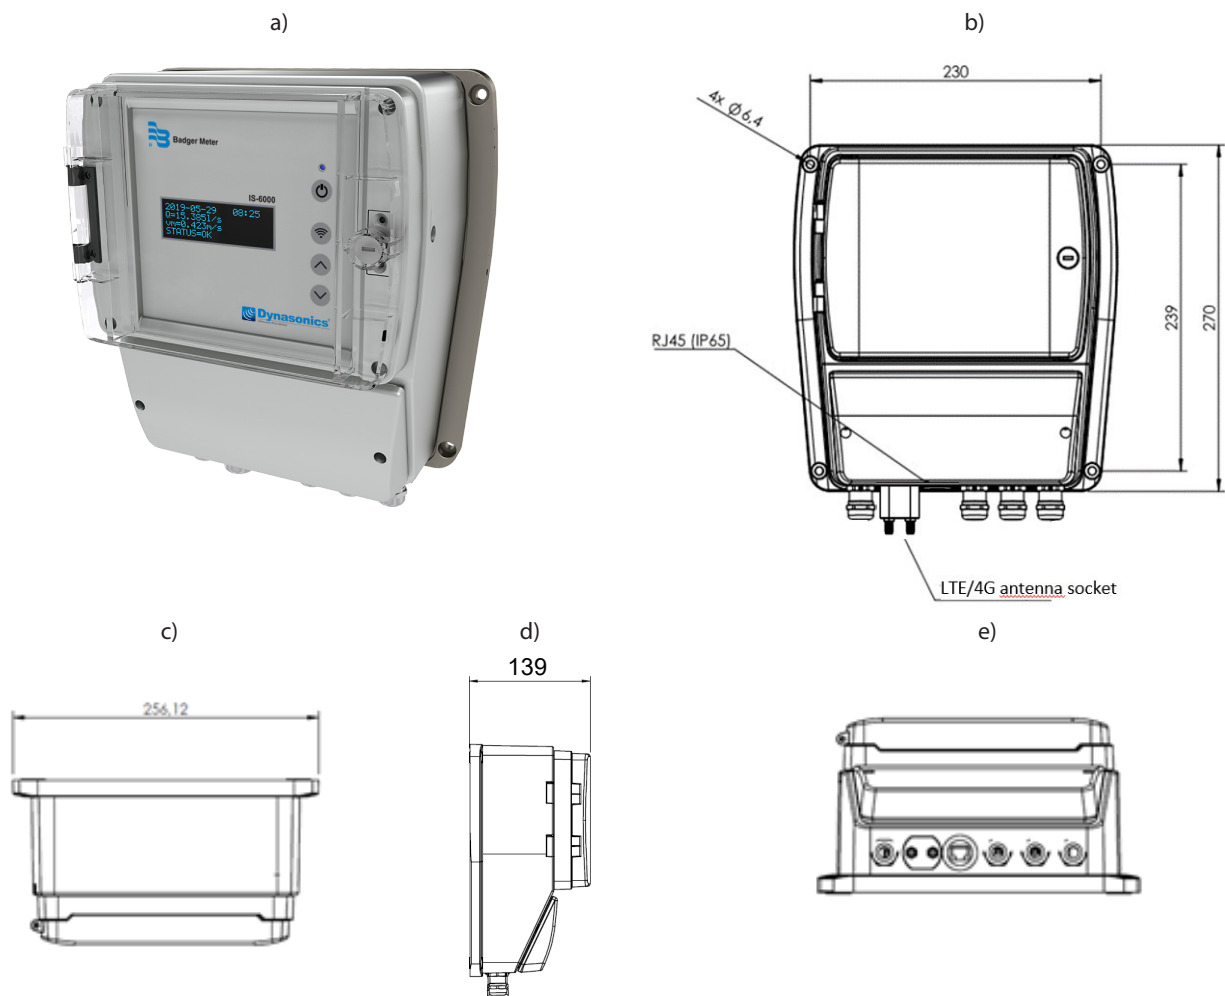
a), b) Vista frontal de la carcasa del transmisor para instalación en pared, dimensiones de la carcasa (en mm)
